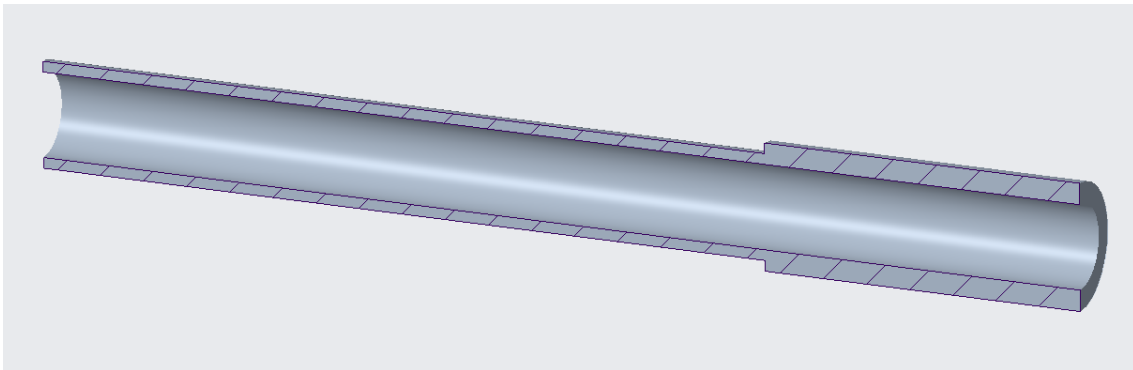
posible eje delantero con un escalonamiento sin el cilindrado interior (corte por el plano medio).
